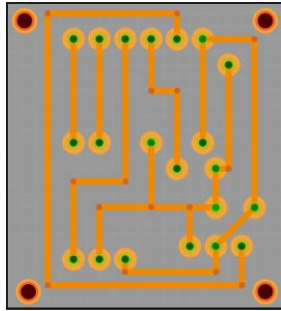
Diseño de tarjeta de microfibra PCB [Elaboración propia].
